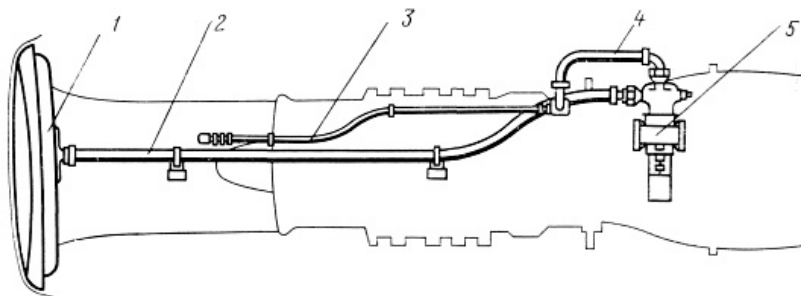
Противообледенительное устройство воздухозаборника правого двигателя: 1 – коллектор (обтекатель воздухозаборника двигателя); 2, 4 – трубопроводы; 3 – шланги; 5 – переключатель воздуха 525А
